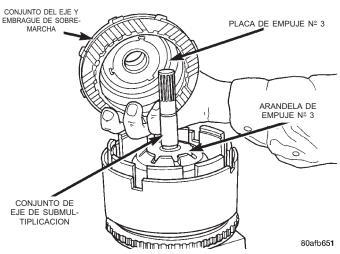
Desmontaje del conjunto del embrague de sobremarcha
